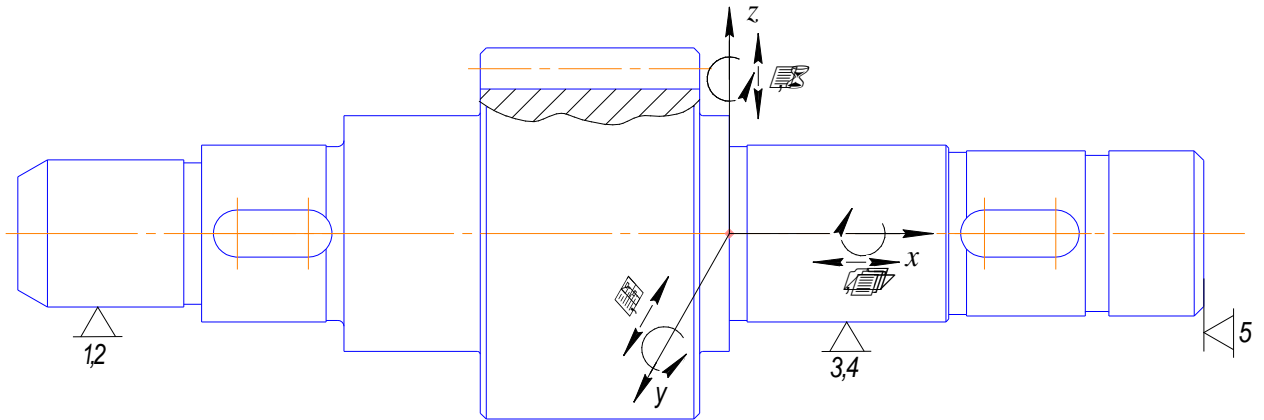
Схема базування валу-шестерні у вузлі
